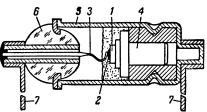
Устройство плоскостного германиевого диода. I — германий; 2 — индий; 3 — верхний токосниматель; 4 — нижний токосниматель; 5 — корпус; 6 — стеклянный изолятор; 7 — ком-
